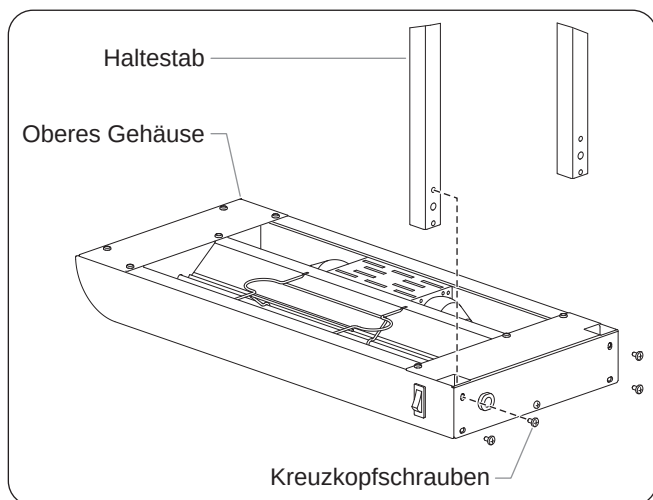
Montage von oberem Gehäuse und Haltestab
